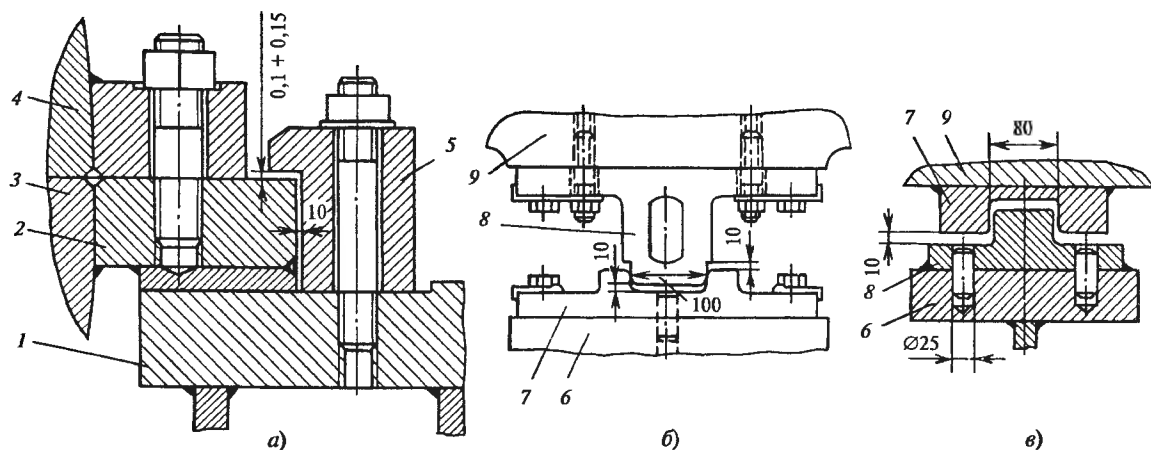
Детали установки обоймы в корпусе ЦНД:
